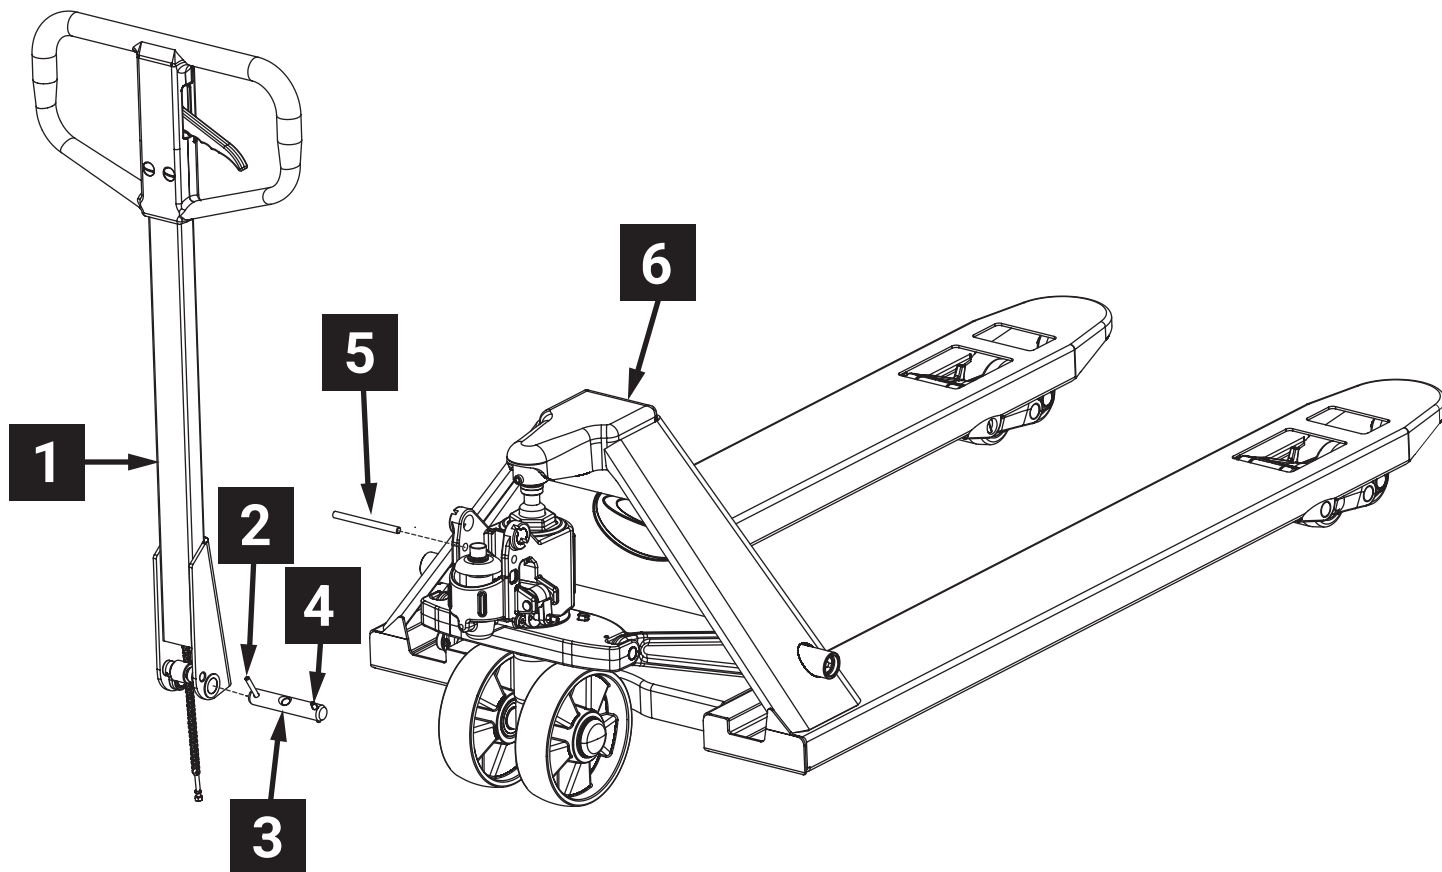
Montagem da Alavanca / Montaje de la Palanca
